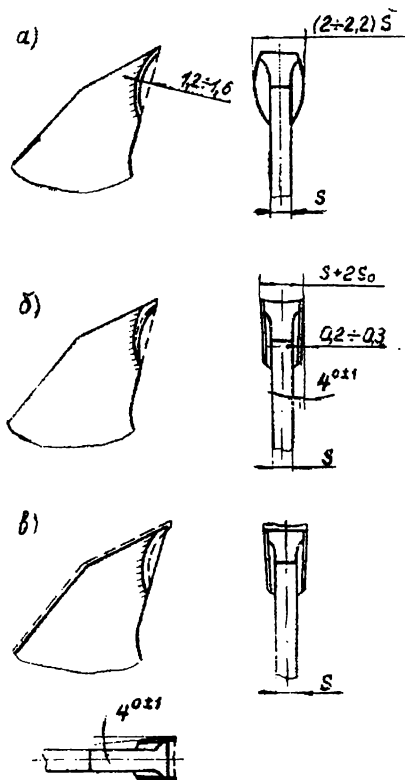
Форма и размеры вершин зубьев рамных пил:
